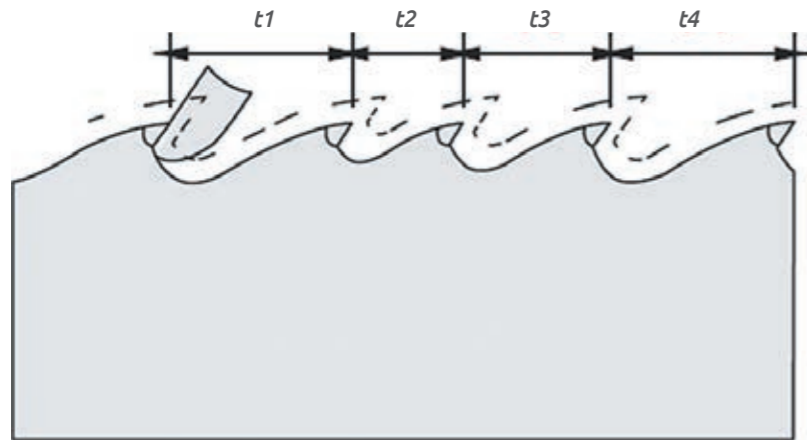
Профиль ленточной пилы с варьированным шагом зубьев и схема движения заточного круга
